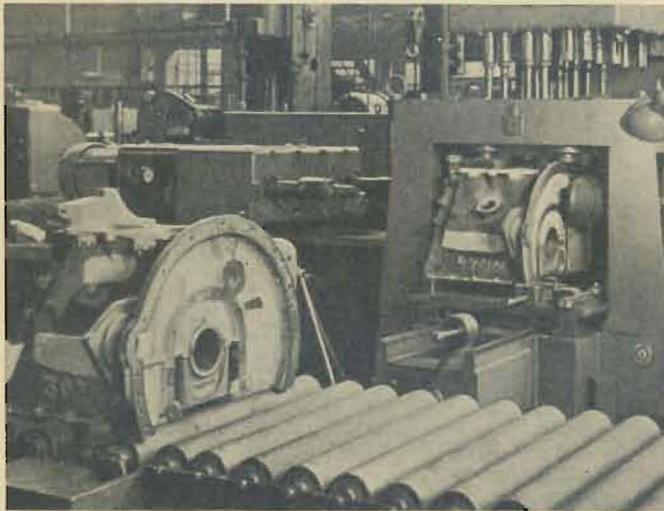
Dreiseitige Sonderbohrmaschine für Nockenwellenbohrung und Stoßführungen
